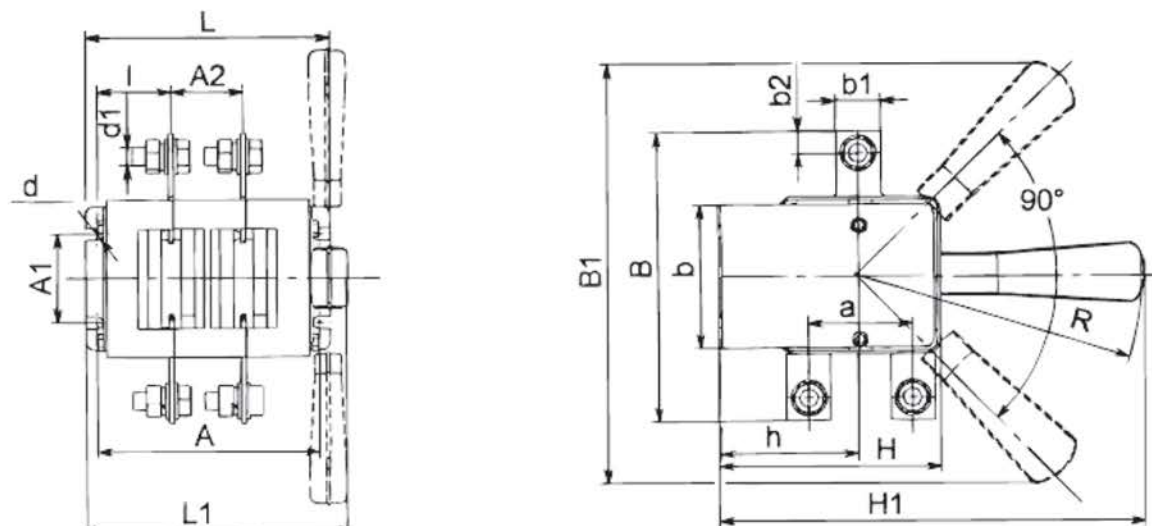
Выключатель-разъединитель двухполюсный на два направления с боковой смещенной рукояткой.
